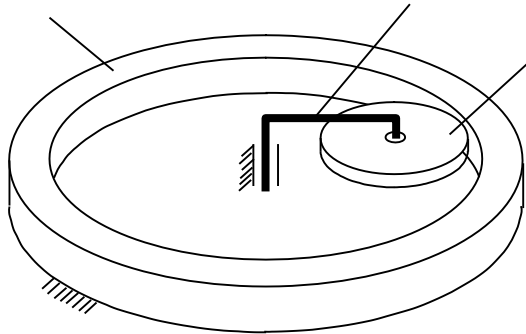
Кинематическая схема заменяющего механизма с внутренним зацеплением для случая остановленного шлифовальника: 1 – подвижное колесо; 2 – водило; 3 – неподвижное колесо
